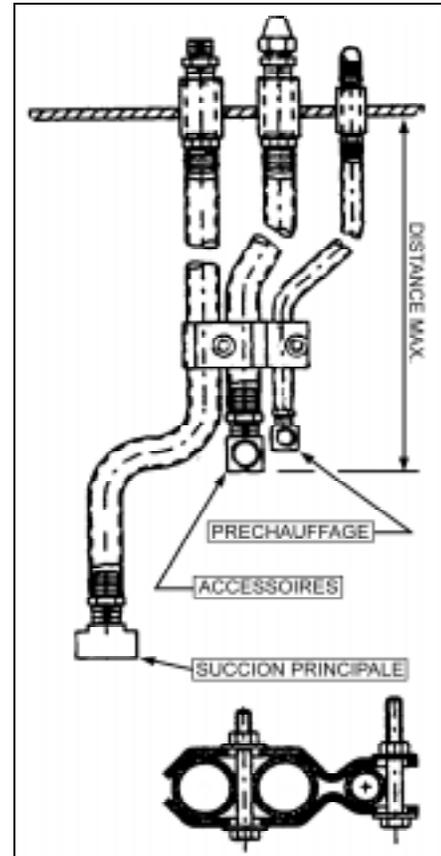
ASSEMBLAGE À TROIS TUYAUX.
